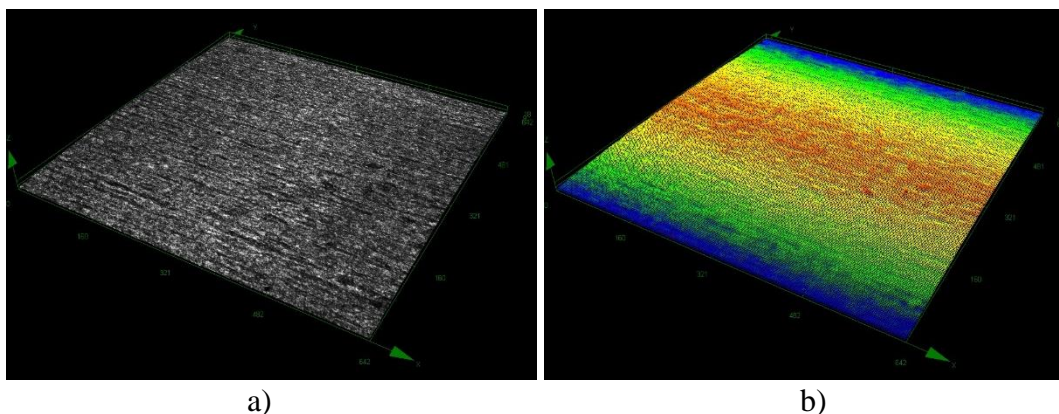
Technicky hladká Inconel 625 a) snímek z laserového mikroskopu zvětšení 430x b) snímek povrchu ze kterého byla počítána struktura povrchu
